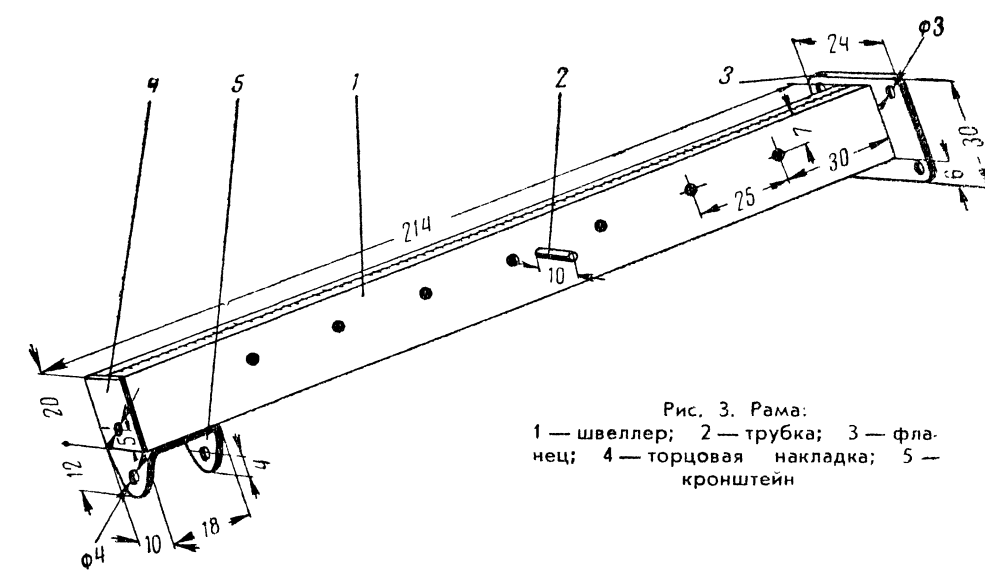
Рама: 1—швеллер; 2—трубка; 3—фланец; 4—торцевая накладка; 5—кронштейн
